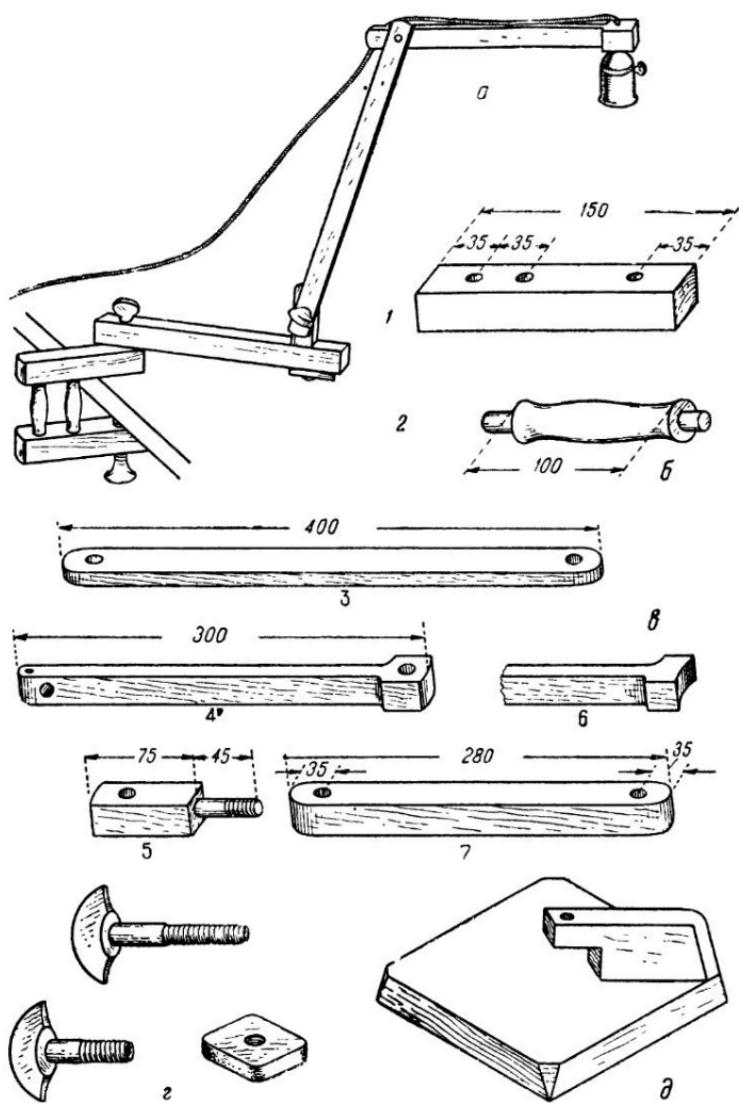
Настольная лампа: а — общий вид; б — детали струбцины; в — детали стойки; г — деревянные винты и гайка; д — подставка.
